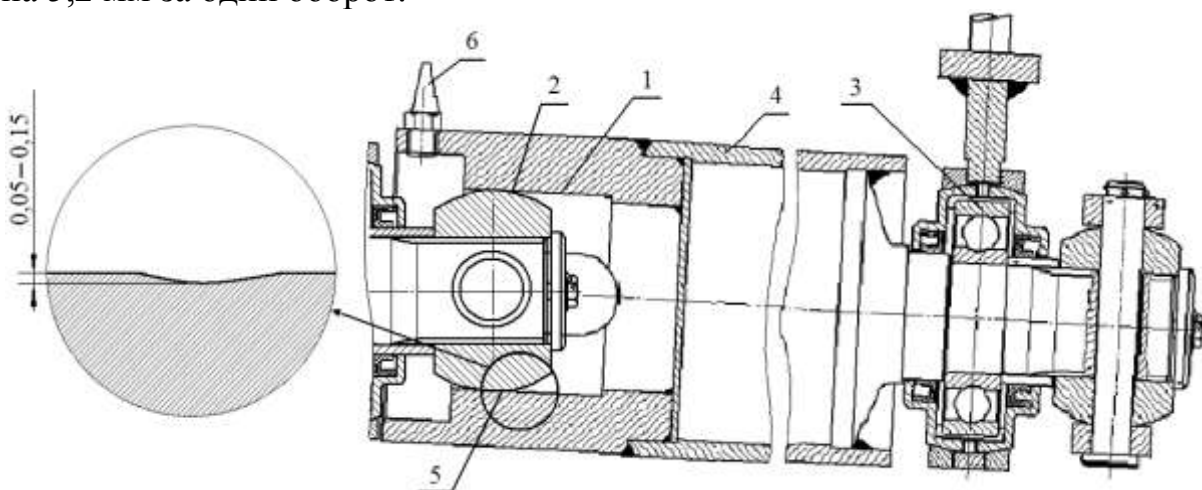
Схема разворота фрезы из-за неровностей на поверхности торфяной залежи и расположения износа на контактной поверхности муфты:
